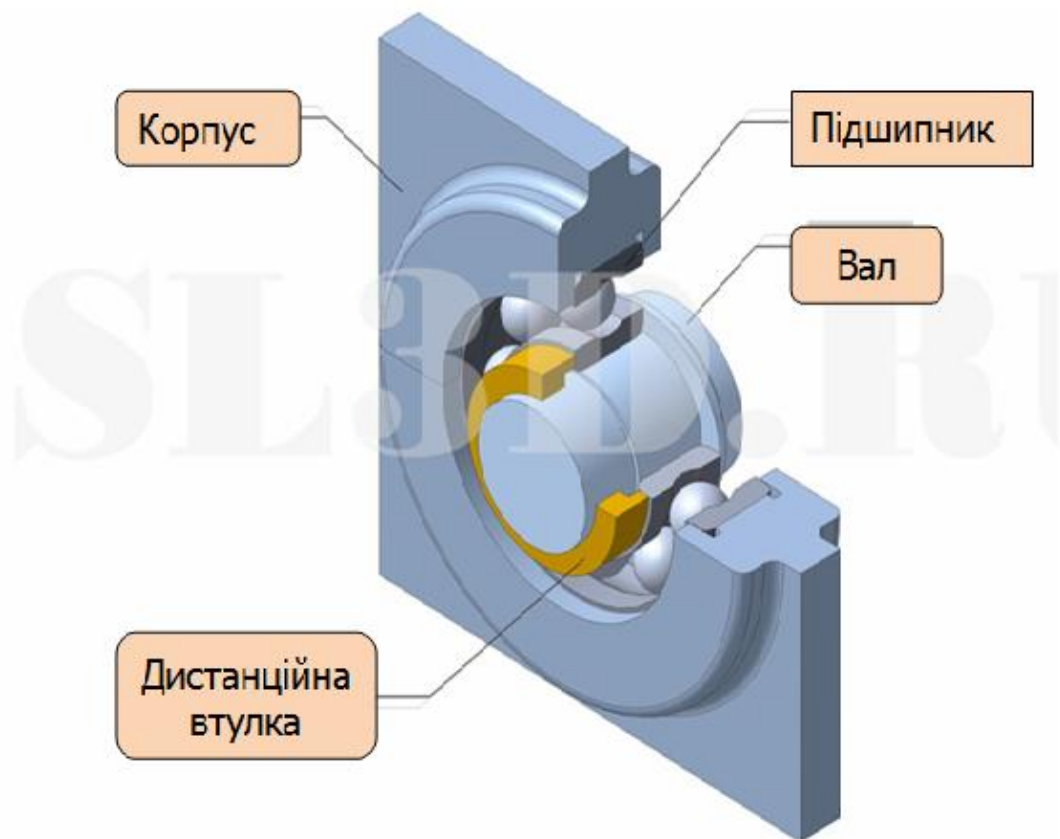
Установка підшипника в кільцеві канавки корпуса
